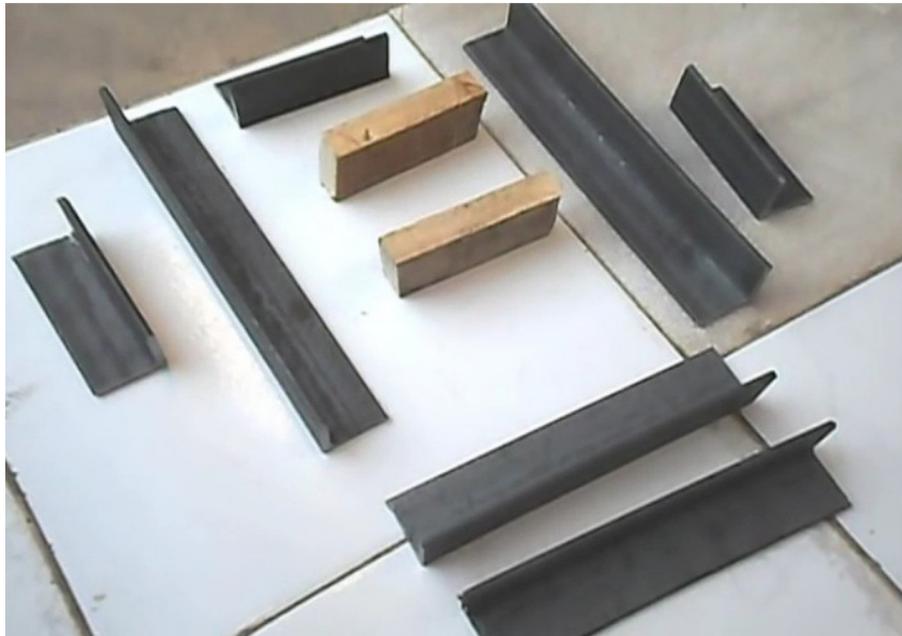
Cantoneiras Cortadas (10, 20 e 25cm).
